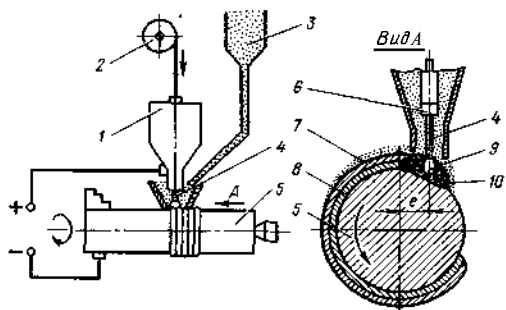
Схема электродуговой наплавки детали под флюсом:
